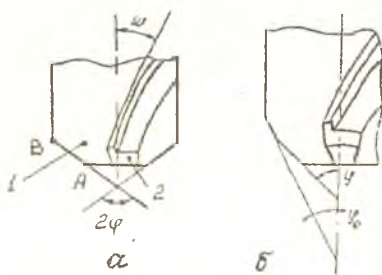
Конструкция режущей части зенкера: а - стандартного; б - с переходной дополнительной кромкой
